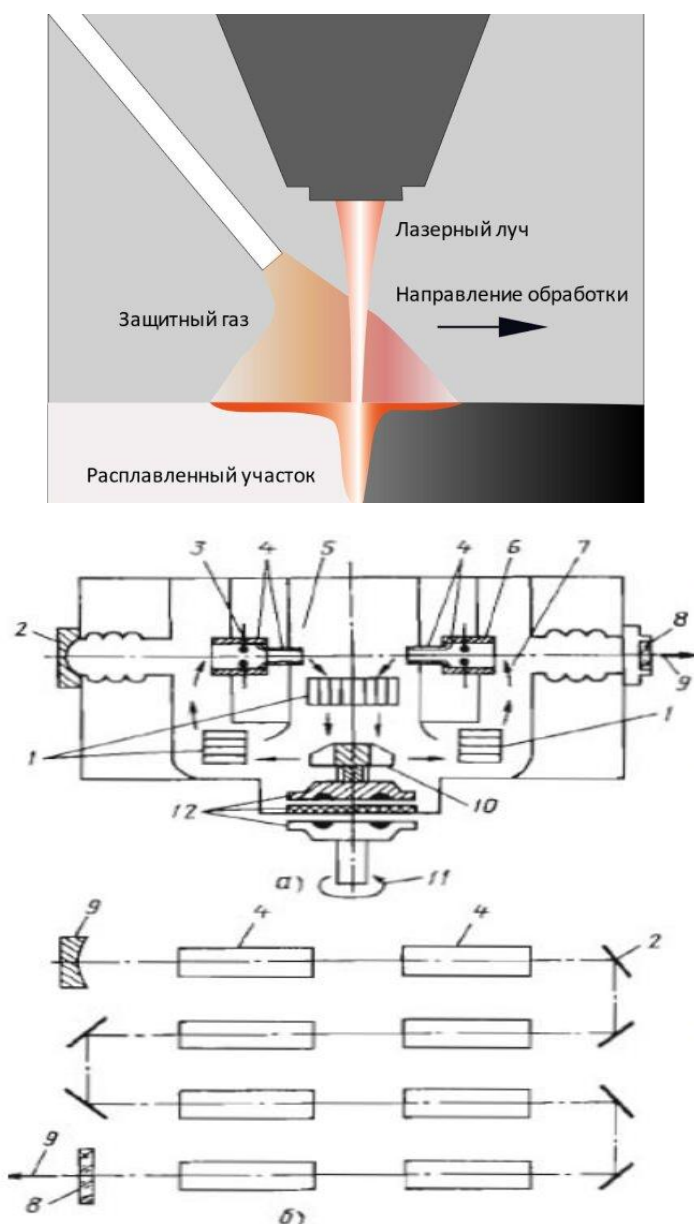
Схема лазера с быстрой продольной прокачкой, используемая в лазерной технологической установке для сварки «Лагус-31»:
